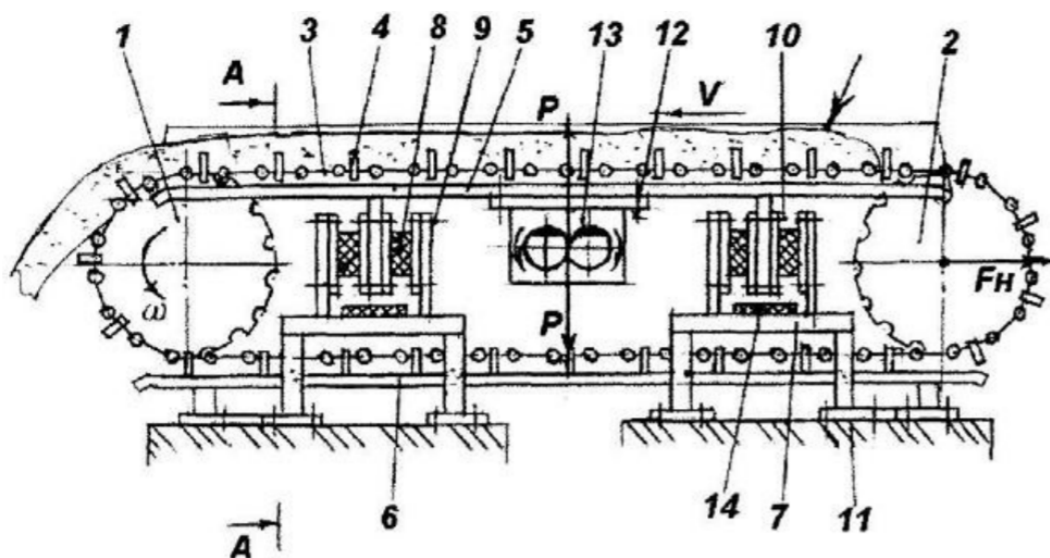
Загальний вид скребкового конвеєра
